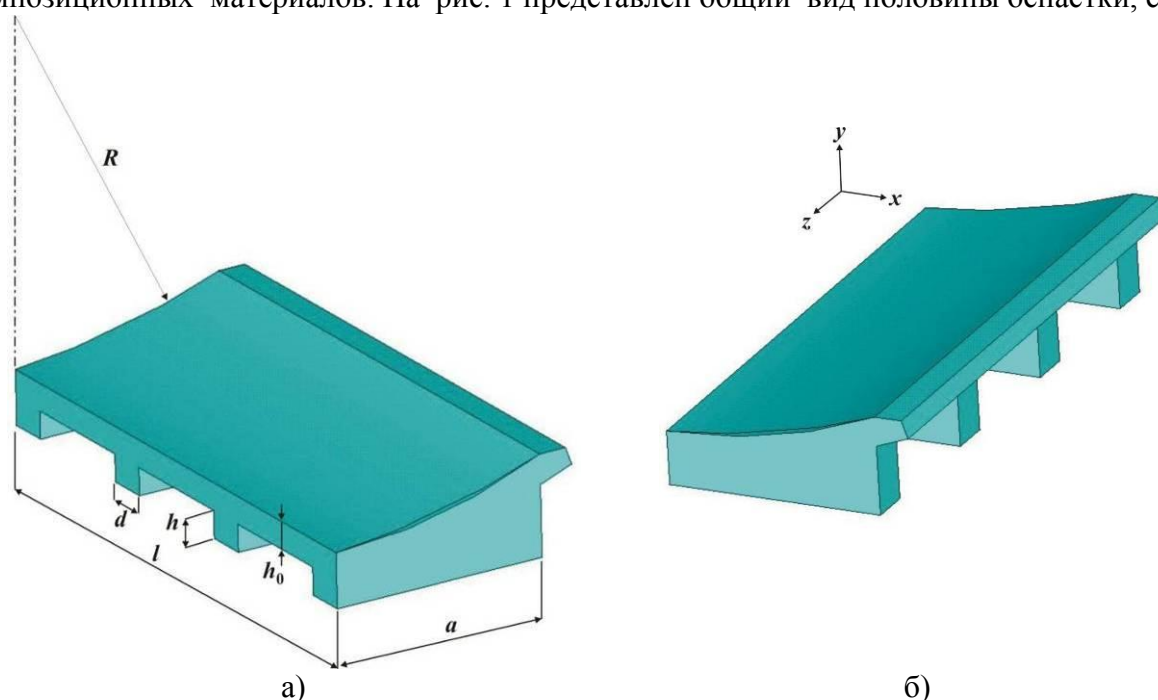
Монолитная оснастка с цилиндрической рабочей поверхностью
